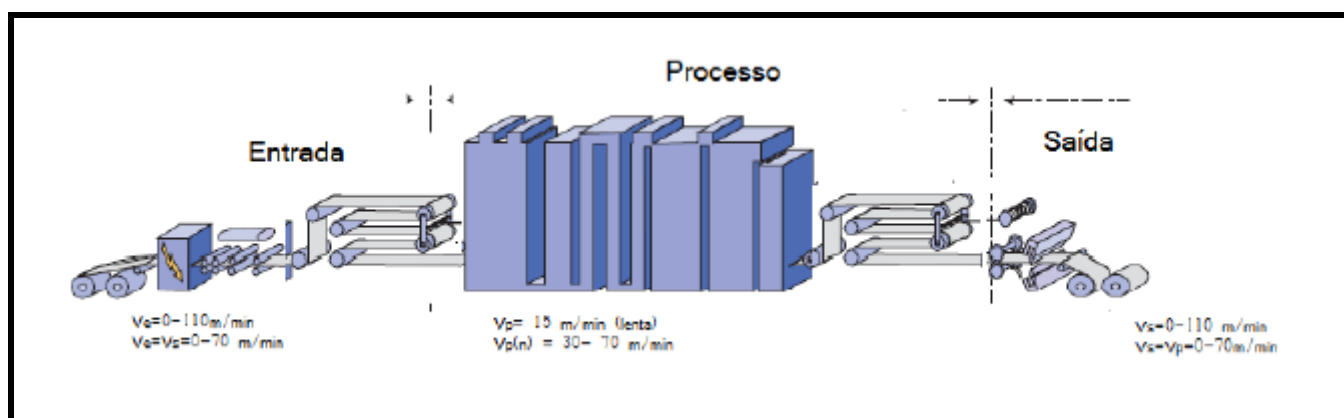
Ilustração geral da linha que tem aproximadamente 300 metros
